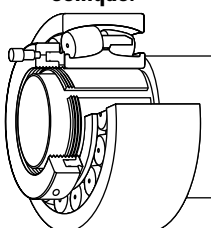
Écrou hydraulique utilisé pour monter le roulement sur un arbre cône.
